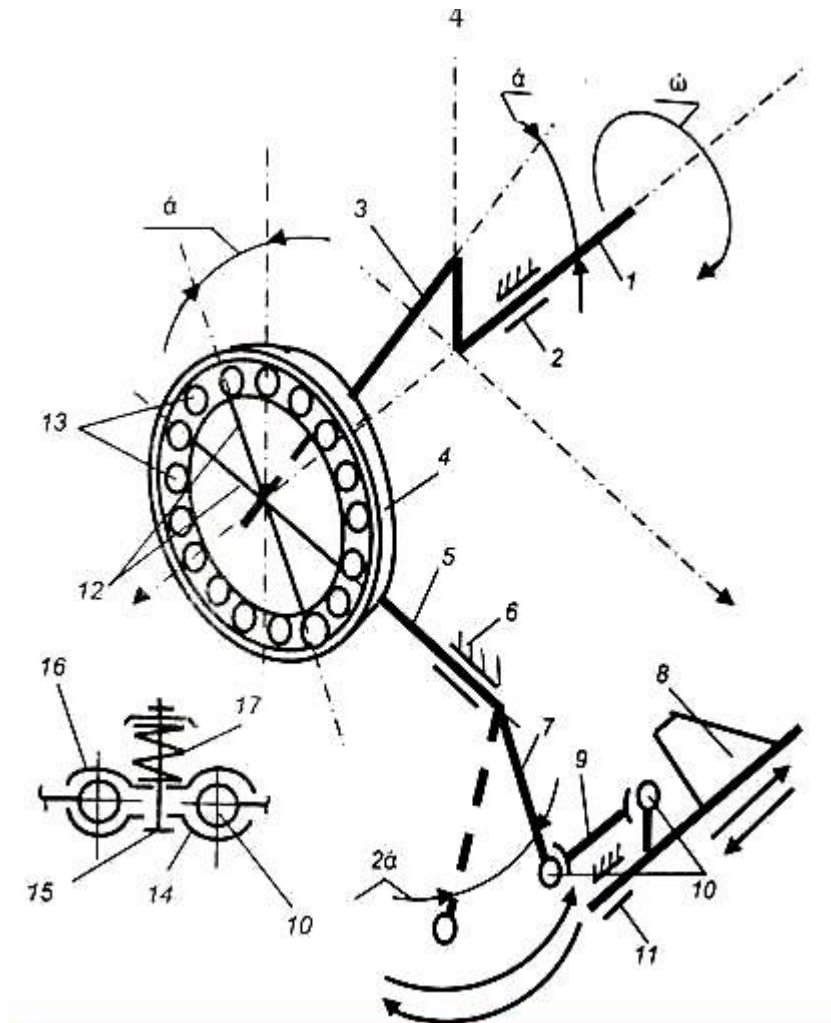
Принципова схема механізму коливної шайби: 1 – ведучий вал; 2,6 - корпус; 3 – коліно ведучого вала; 4 – обичайка; 5 – вал ведений; 7 – водило; 8 – ніж; 9 – ланка сполучна; 10 – кульові шарніри; 11 – напрямна головки ножа; 12 – шайба; 13 – підшипник кочення; 14, 16 – щічки; 15 – болт стяжний; 17 – пружина.
